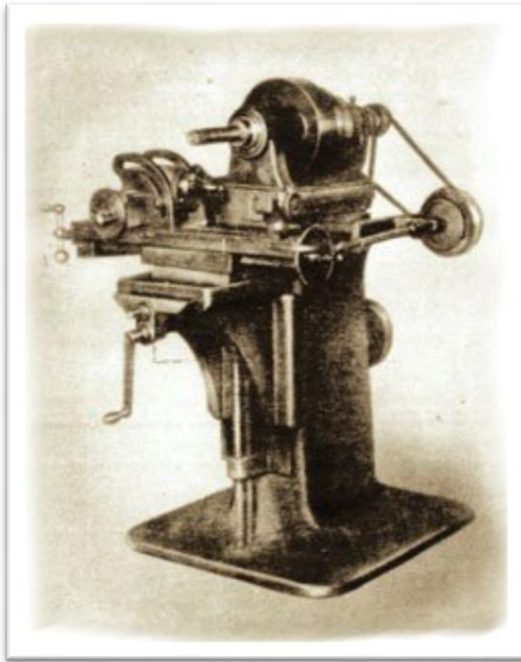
Fresadora Brown&Sharpe 1861 [3]
